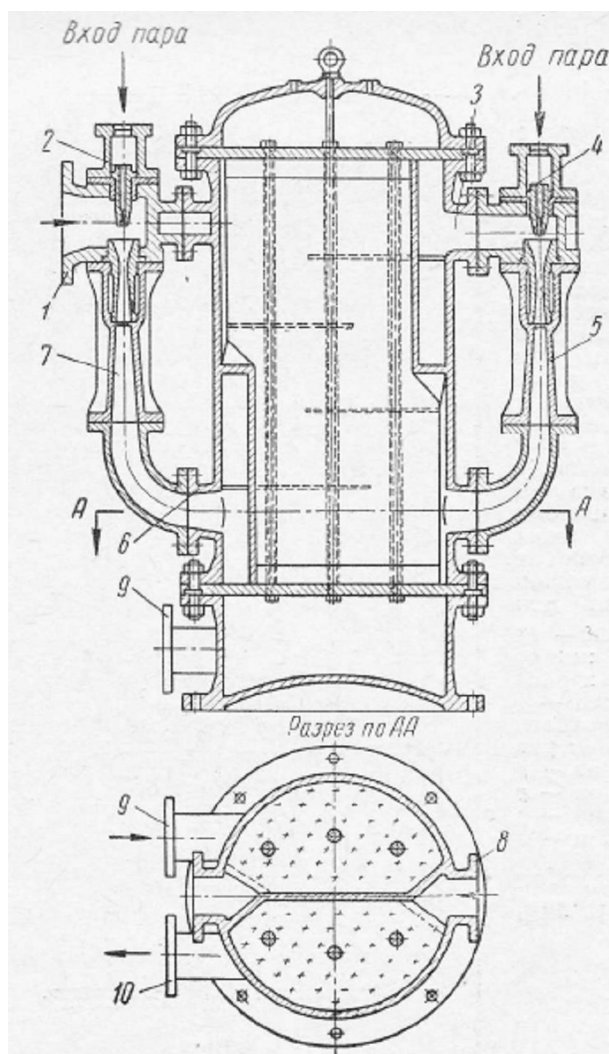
Двоступеневий однокорпусний пароструйний ежектор з прямими трубками:
